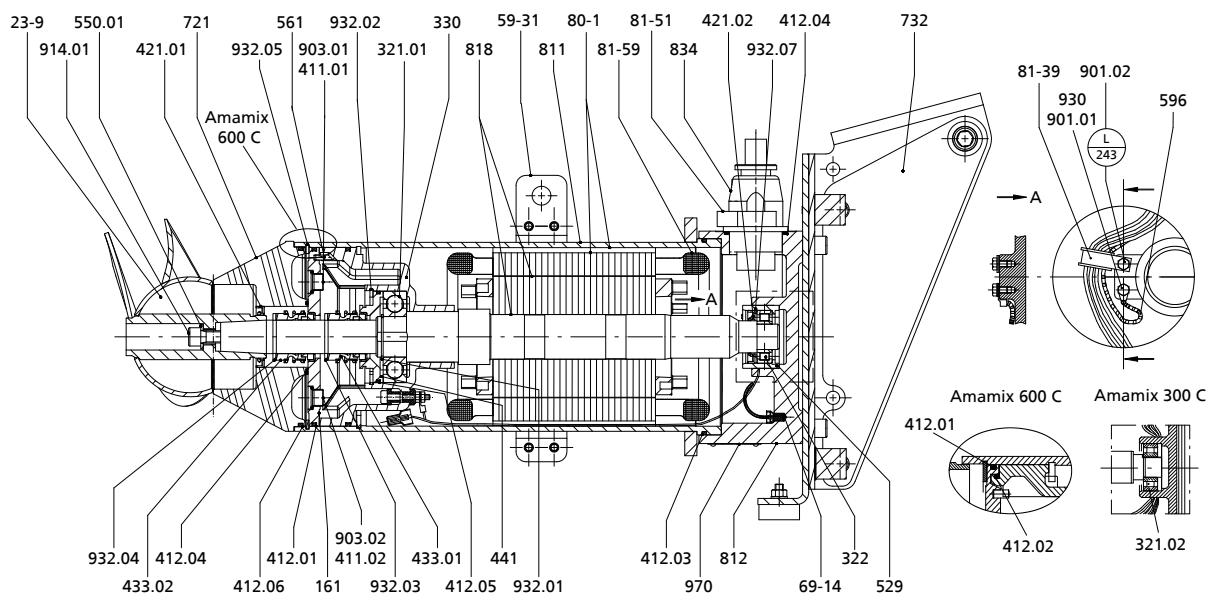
Чертеж общего вида Атаміх 200, материал корпуса двигателя – серый чугун
